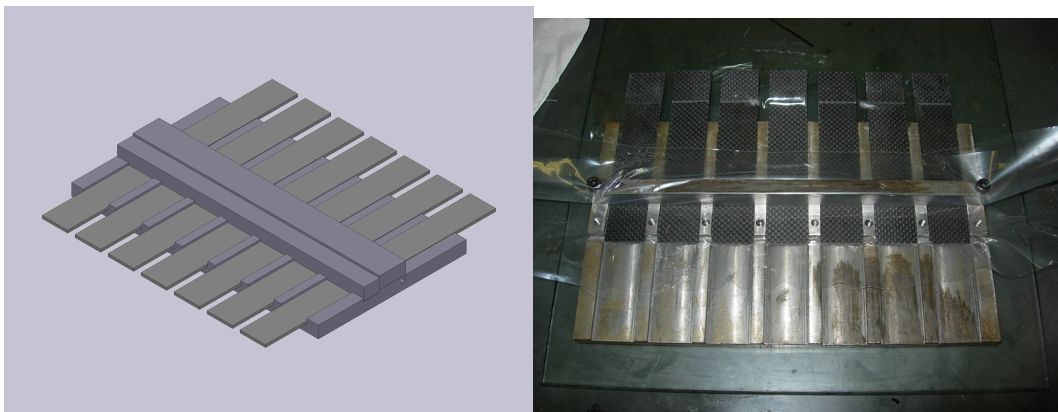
Dispositivo-guia em aço para colagem dos CP's de juntas *single-lap
